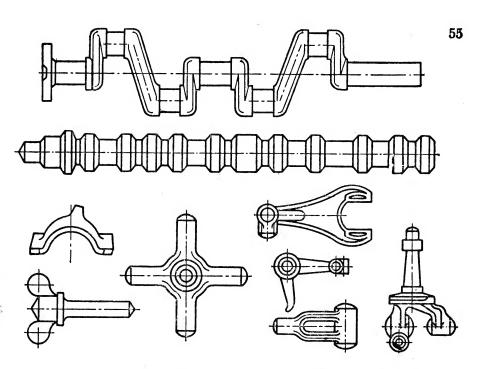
Заготовки, получаемые ковкой и штамповкой.
